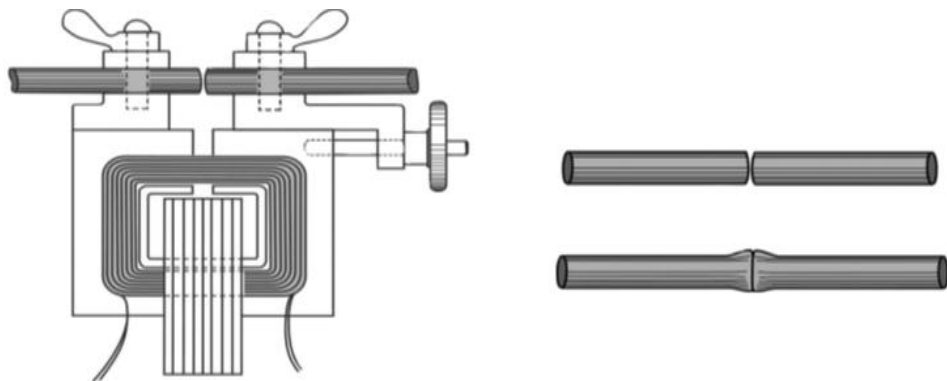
Transformateur de Thomson pour le soudage électrique par résistance.
